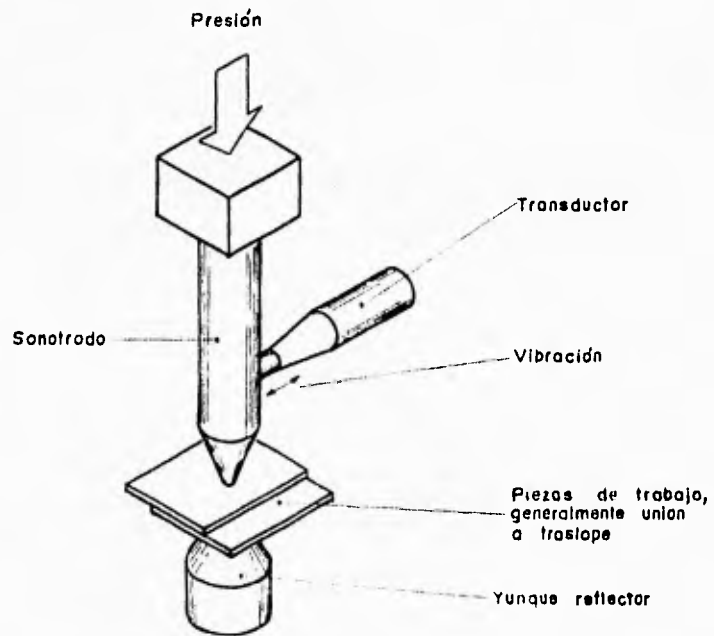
Soldadura por ultrasonido (USW)
